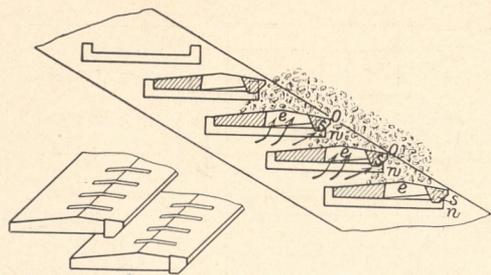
Rostplatten. Bauart: Strube-Lange. D. R. P.
